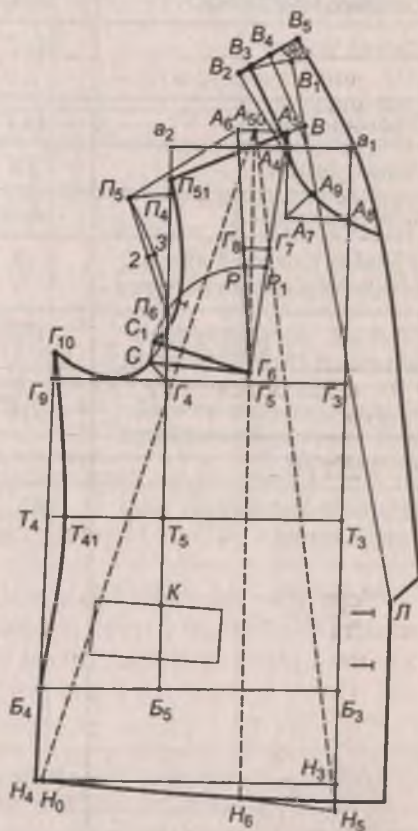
Чертеж конструкции жакета свободной формы (полочка) с воротником покроя шаль
